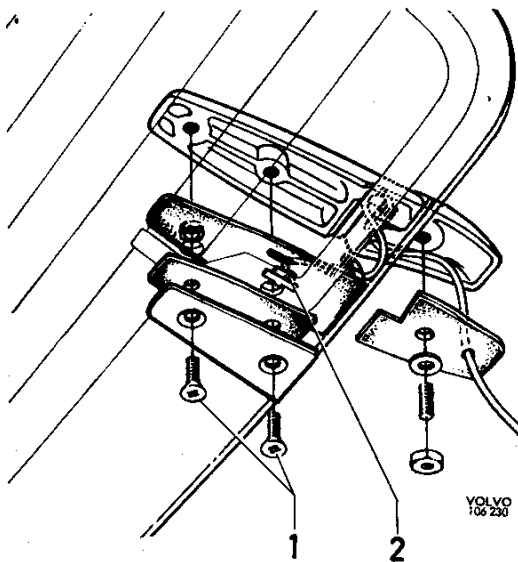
Heckklappenscharnier, 1800 ES, zerlegt
